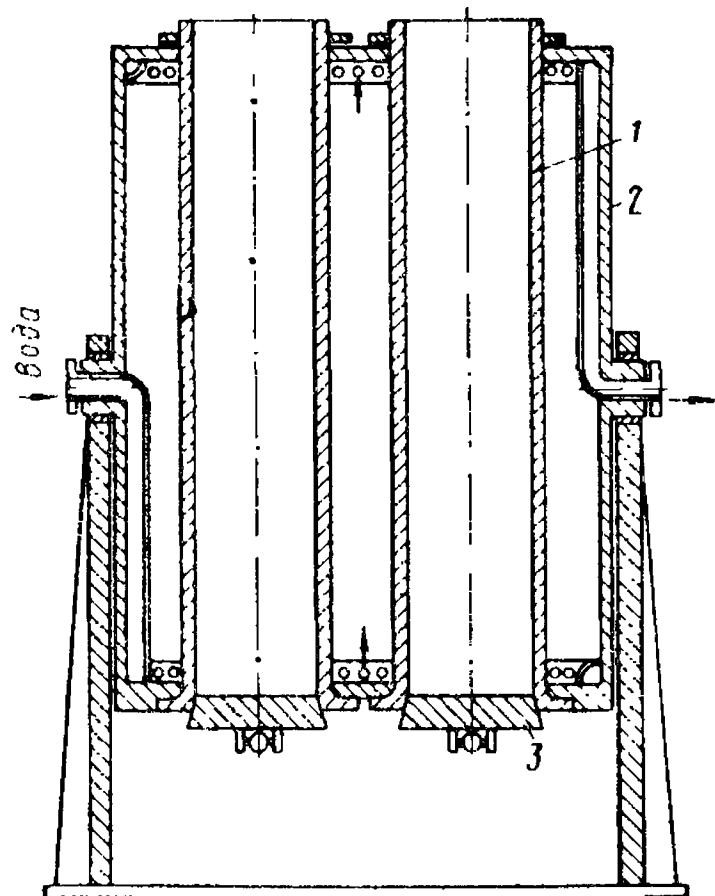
Вертикальная цельнометаллическая изложница для отливки цилиндрических слитков:
